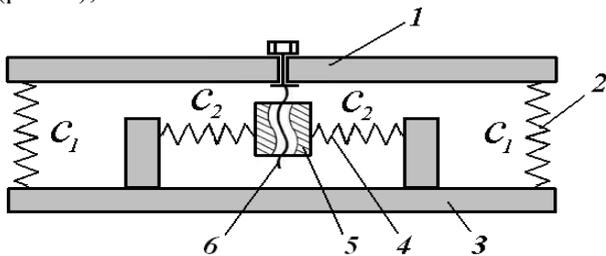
Схема конструкции второй ступени рессорного подвешивания с применением регулятора корректора жесткости: 1 – грузовая платформа, 2 – пружины второй ступени подвешивания, 3 – опорная платформа, 4 – пружины корректора жесткости, 5 – гайка регулировочная, 6 – винт регулировочный.
